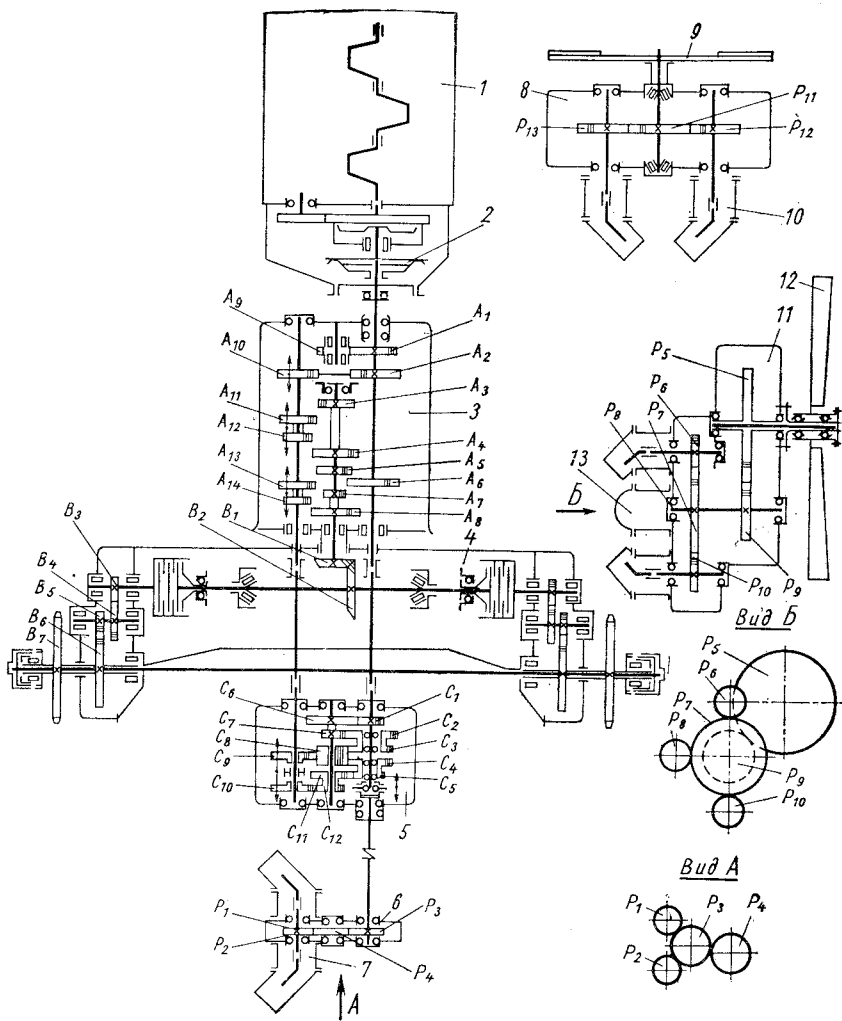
Кинематическая схема силовой передачи каналочистителя КОБ-1,5:
